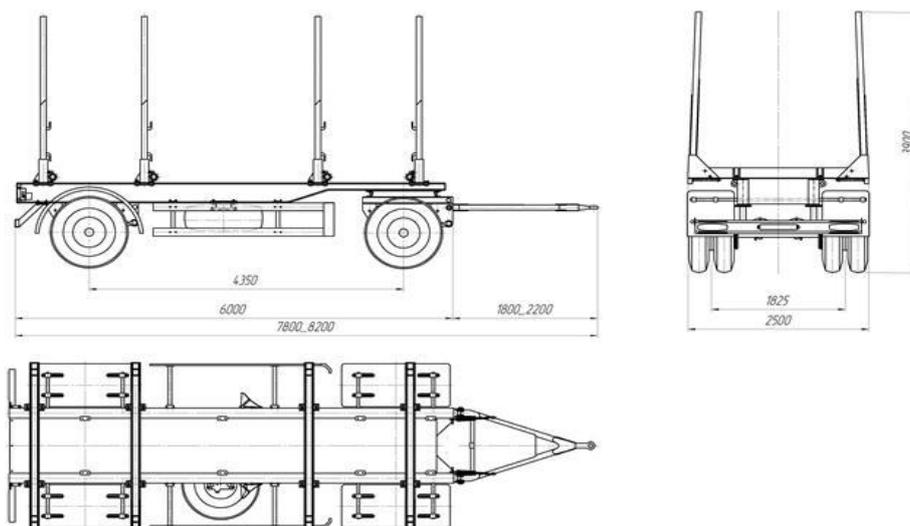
Внешний вид сортиментовозного прицепа 600220
